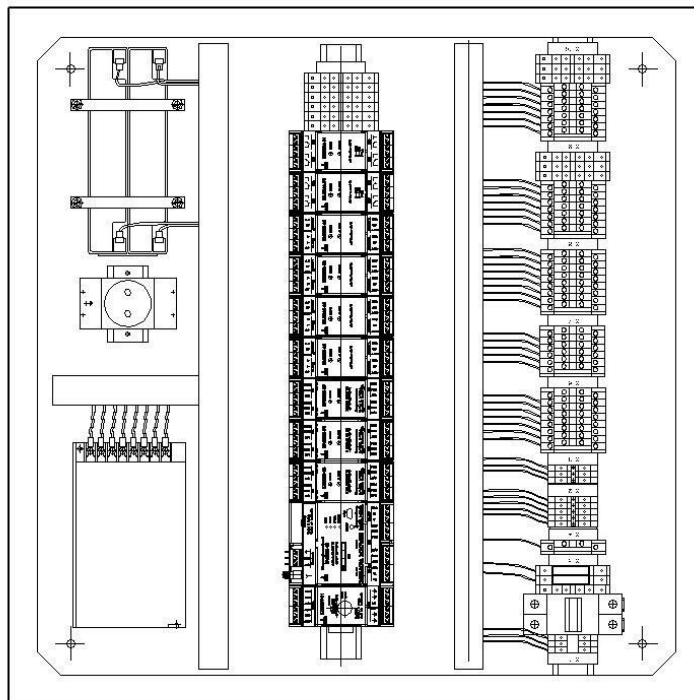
Внешний вид и габаритные размеры системы «АСДУК-Э»
